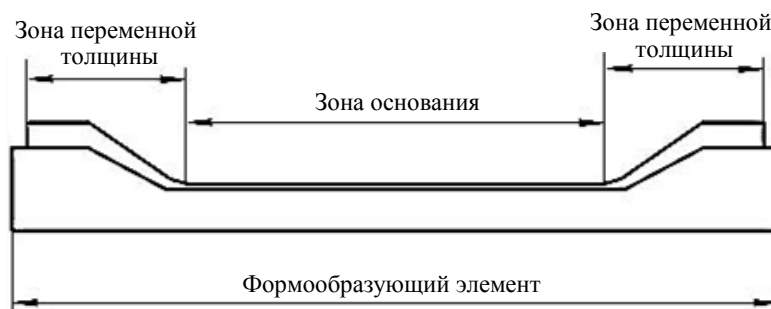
Эскиз формообразующего криволинейного элемента и конструктивно-подобного образца
